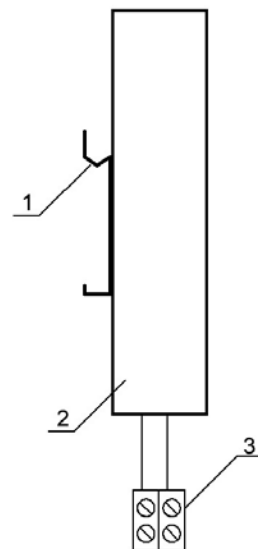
Вид сбоку. 1. Крепление к DIN-рейке. 2. Корпус нагревателя. 3. Клемма питания.
